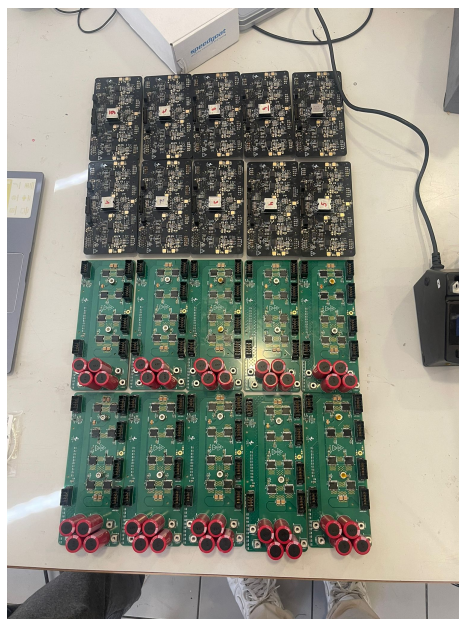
Proceso de soldadura LDU+LPU.
